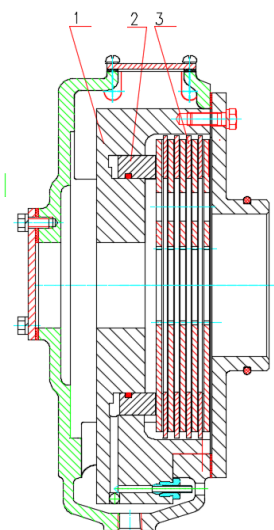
ТМ прямого действия: 1 – корпус; 2 – кольцевой поршень; 3 – пакет дисков
